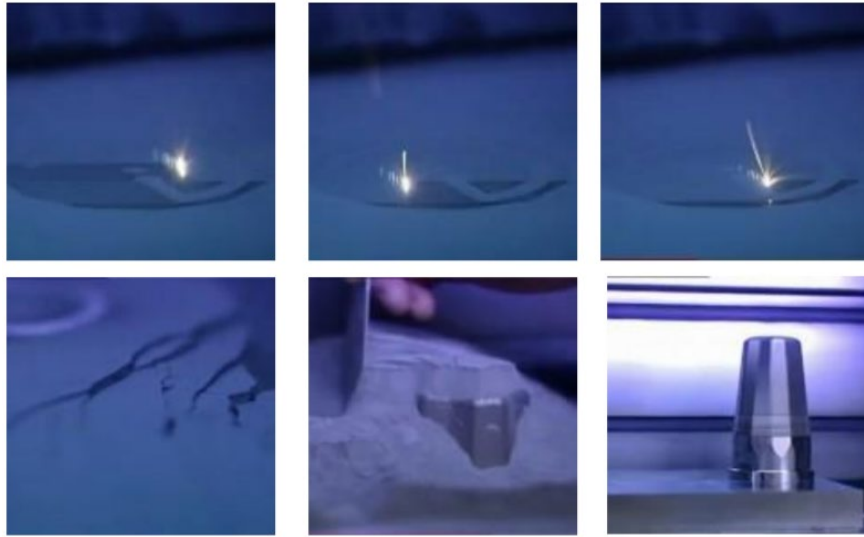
Los diferentes componentes de una impresora de Sinterizado Selectivo por Laser (SLS)
